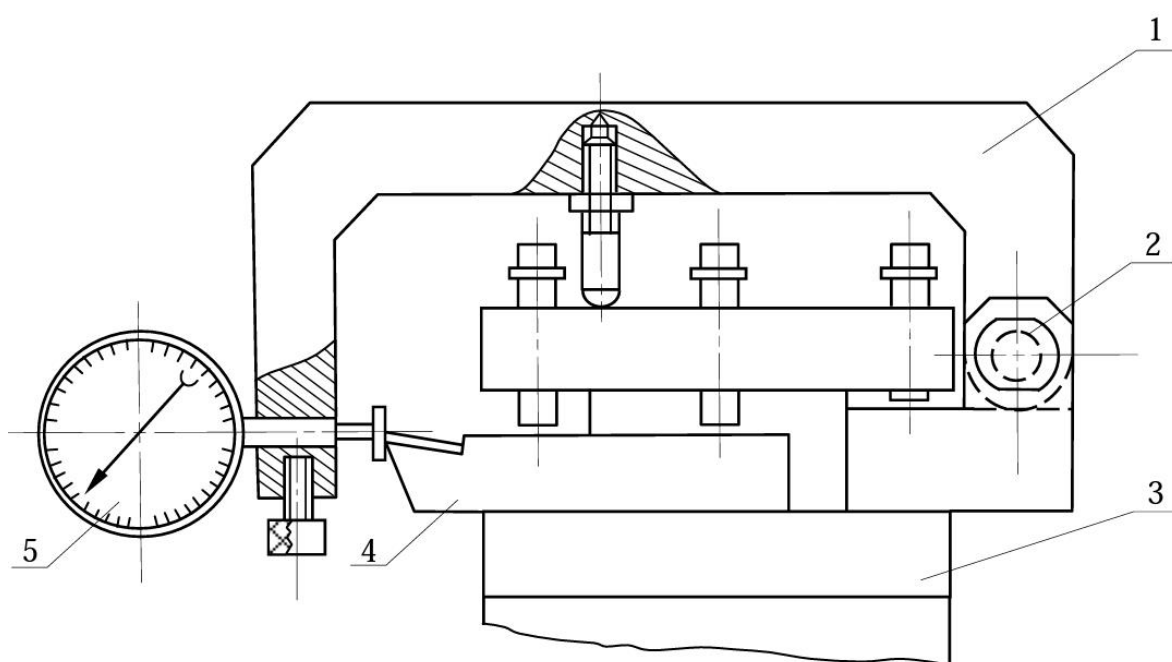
Пристрій для вимірювання розмірного зношування вершини леза різального інструменту. 1- корпус пристрою; 2 - вісь повороту корпусу; 3 - різцетримач; 4 - різець; 5 - індикаторний вимірний пристрій
